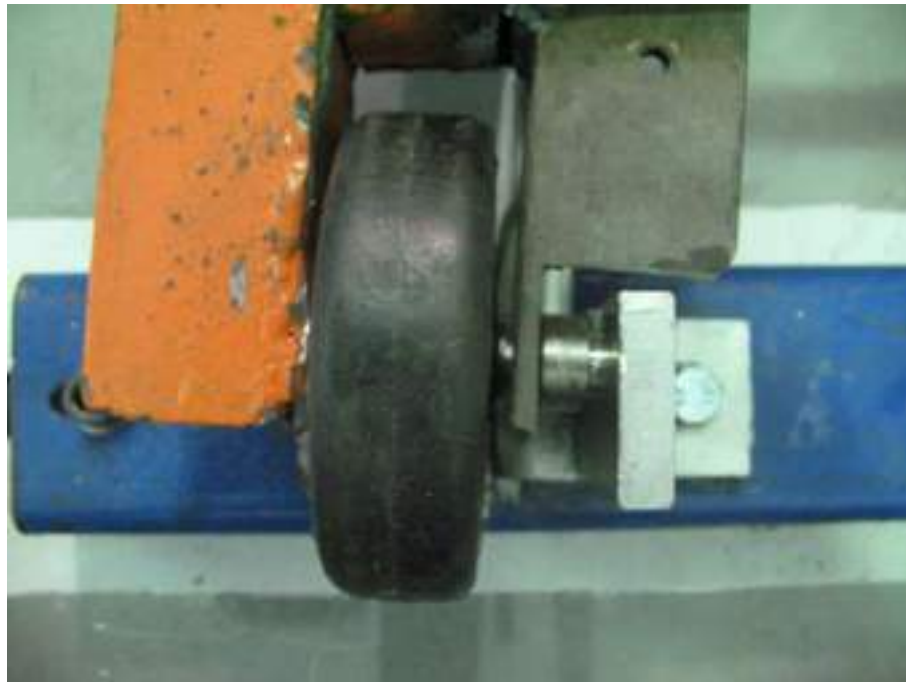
Lado esquerdo da amostra 2 após ensaio.
